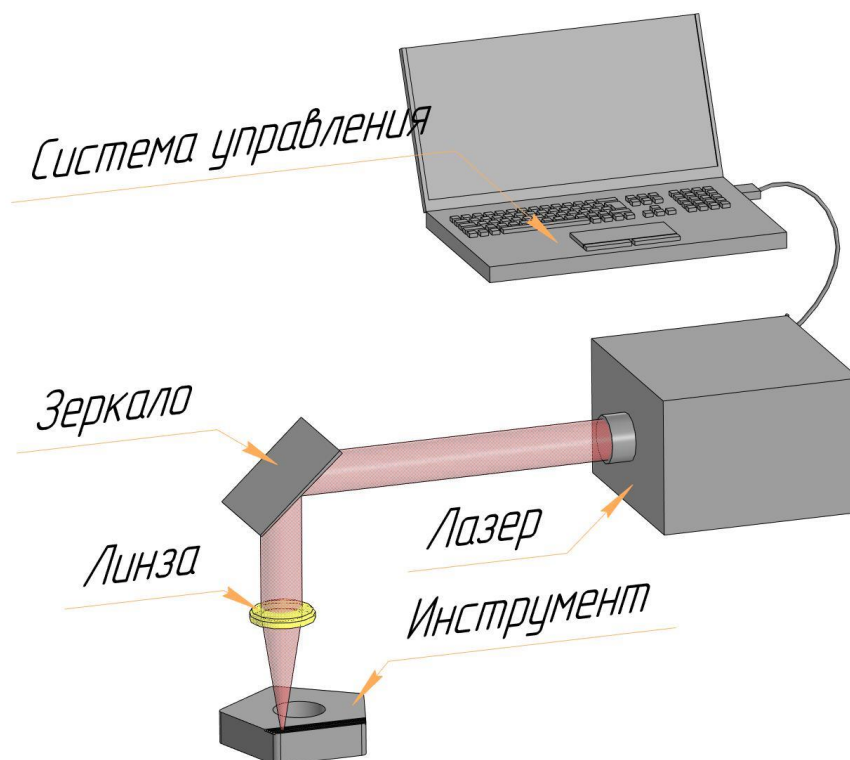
Схема обработки металлорежущего инструмента лазерным излучением
